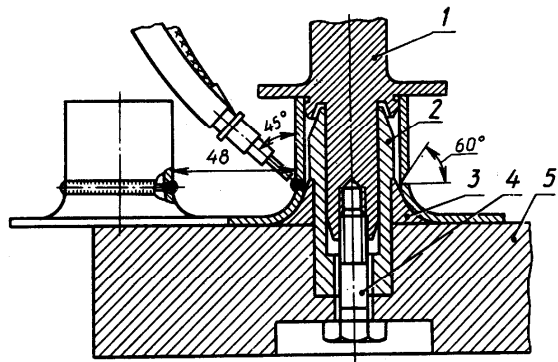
Приспособление для сборки и сварки патрубков
